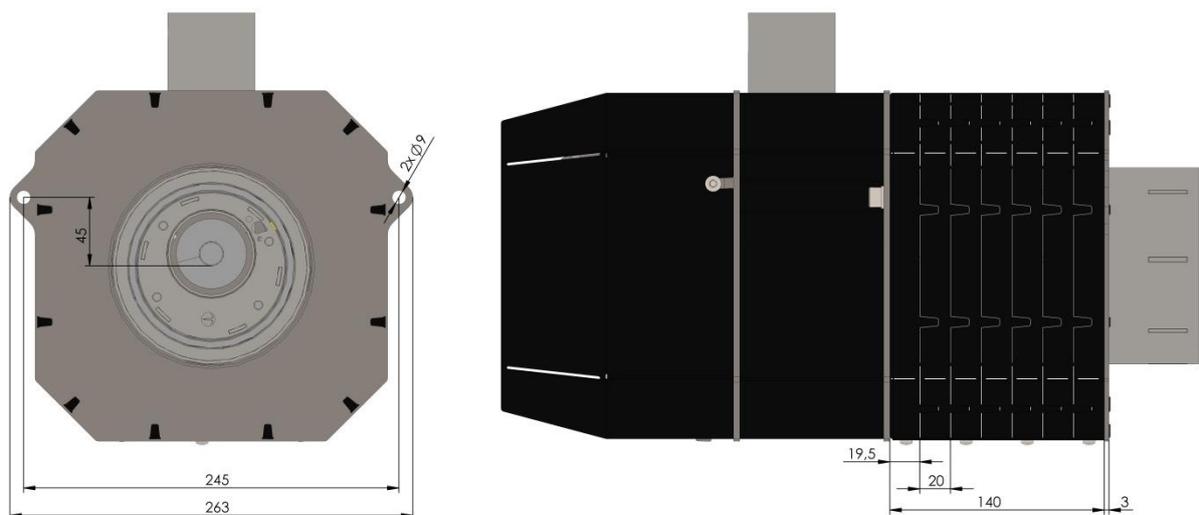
Ansicht des Brenners 5-20 kW mit einem Wärmedämmmantel und einer Montageplatte
